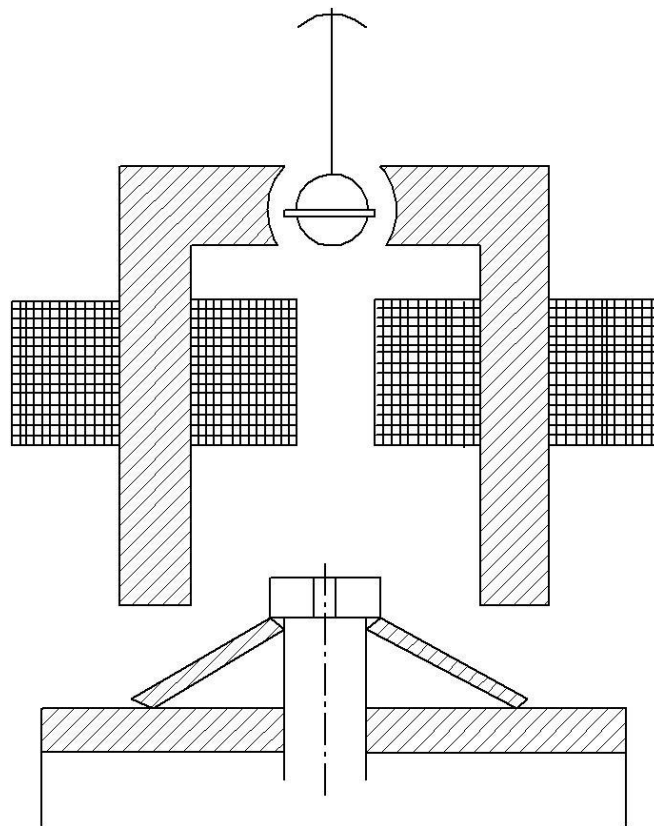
Вигляд різьбового з'єднання з конічною шайбою
